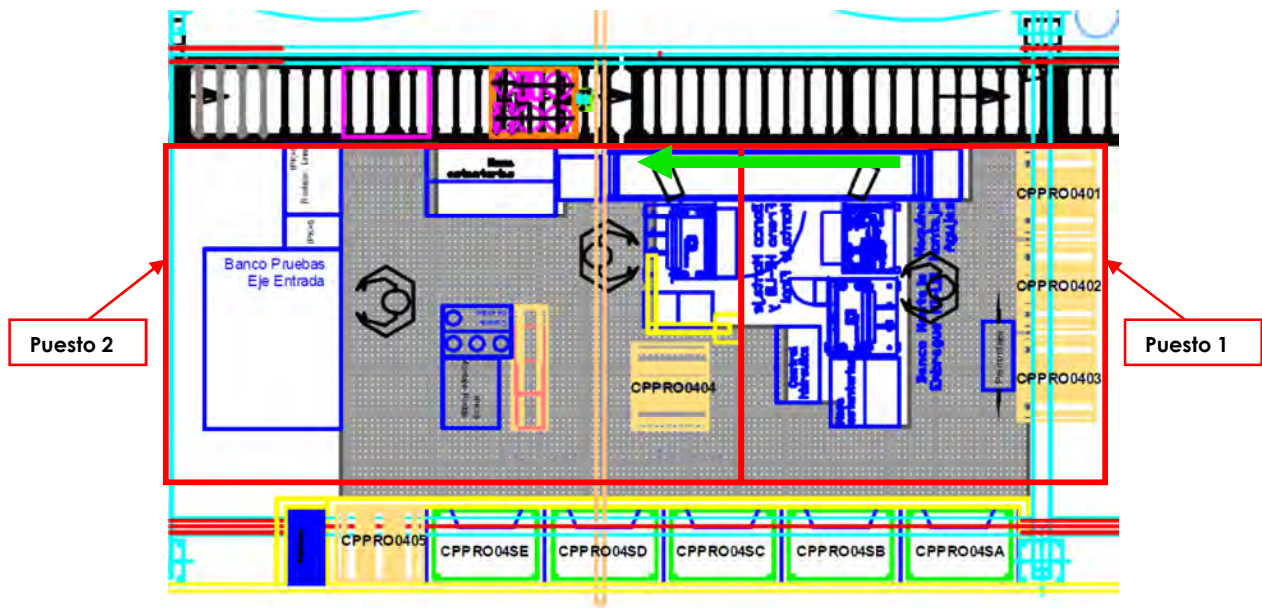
H LAYOUT DEL PREMONTAJE EJE DE ENTRADA
